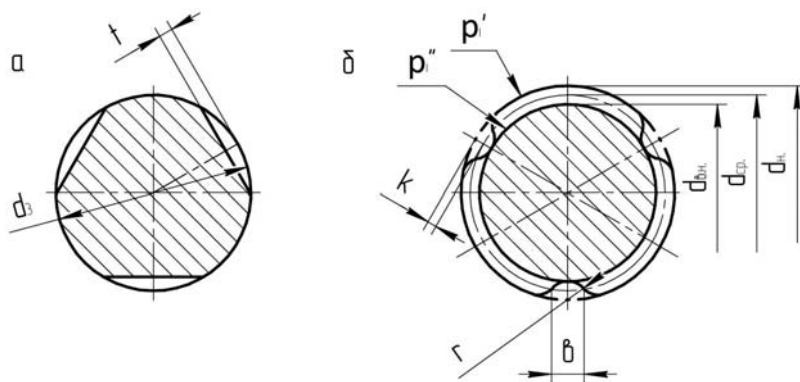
Поперечные сечения рабочей части трехгранных заготовок ПДМ: а – начальное, перед формированием резьбового профиля; б – после накатывания резьбового профиля на рабочей части
